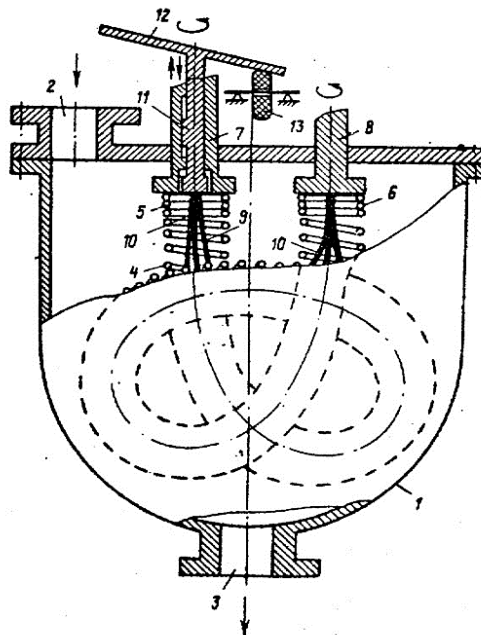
Змішувач: 1 – корпус; 2 - завантажувальний патрубок; 3 - розвантажувальний патрубок; 4 - робочий орган; 5,6 - кінці спіралі; 7 - основний вал; 8 - додатковий вал; 9 - пружні елементи; 10 – пакет; 11 - допоміжний вал; 12 - обмежувальний диск; 13 – ролик
